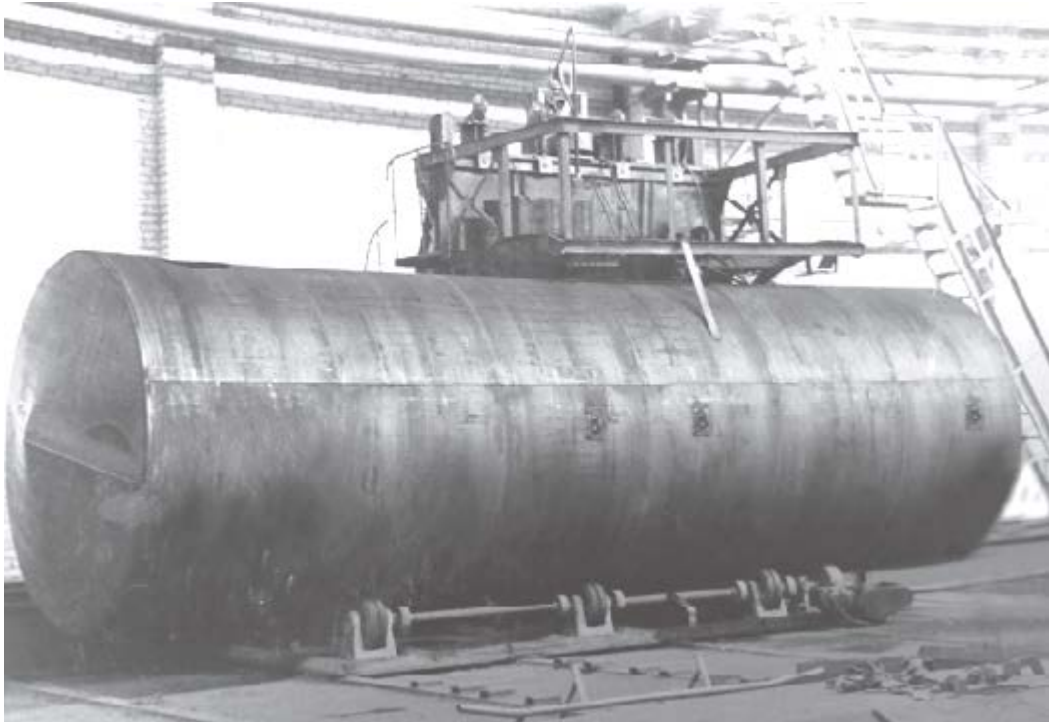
Схема стенду автоматичного зварювання горизонтальних резервуарів
